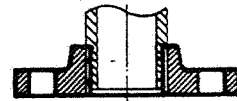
Attacco fra tubo e flangia a collare filettati.
